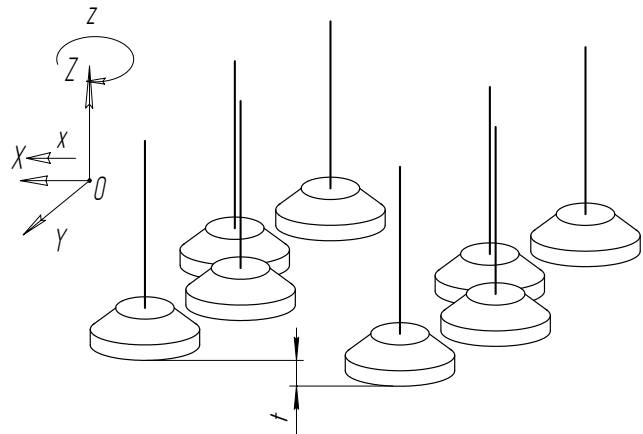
Схема движений абразивного инструмента при многоинструментальной параллельно-последовательной обработке двумя группами инструментов
